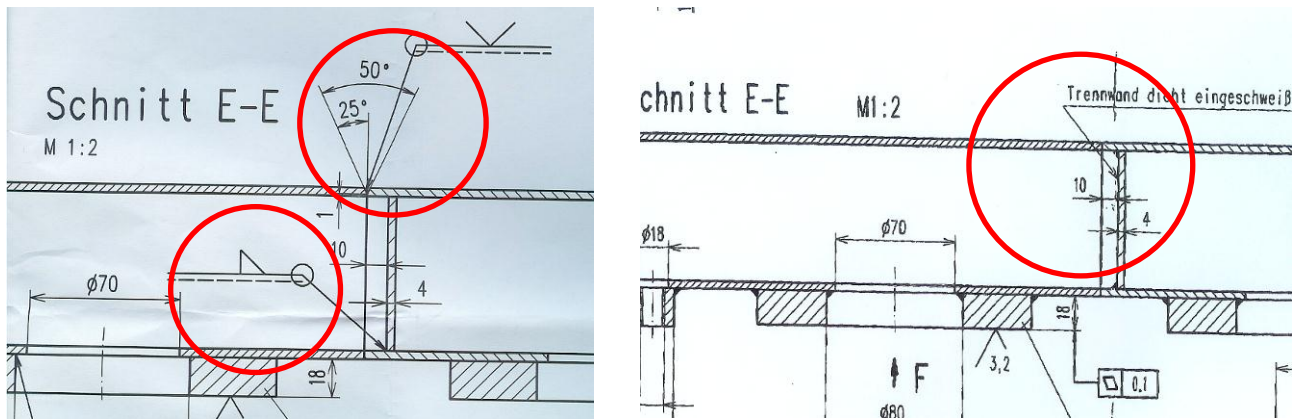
Zeichnung mit exakten Vorgaben - rechte Seite ohne schweißtechnische Angaben
